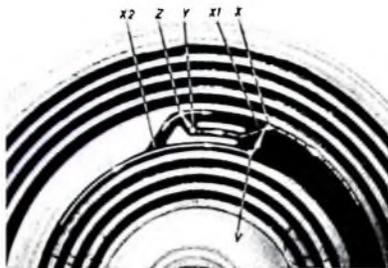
Ausschnitt aus der Rillenscheibe (----- = Wege des Fühlstiftes)
